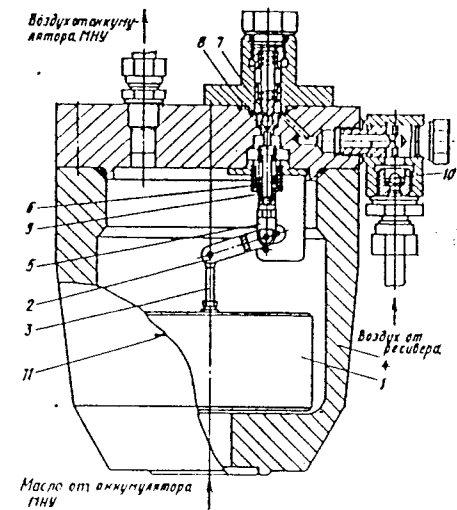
Регулятор уровня масла РУМ-3: 1 — груз; 2 — рычаг; 3 — стяжка; 4 — корпус; 5 — толкатель; 6 — пружина; 7, 10 — шарик; 8 — кольцо; 9 — гайка; 11 — риска
